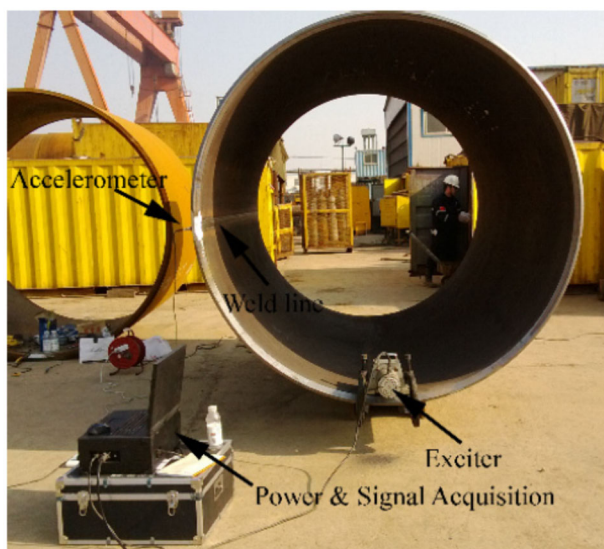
Werkstück zur Untersuchung des Vibrationsentspanns und Wärmebehandlung (geschweisster Stahl) (aus [76])
